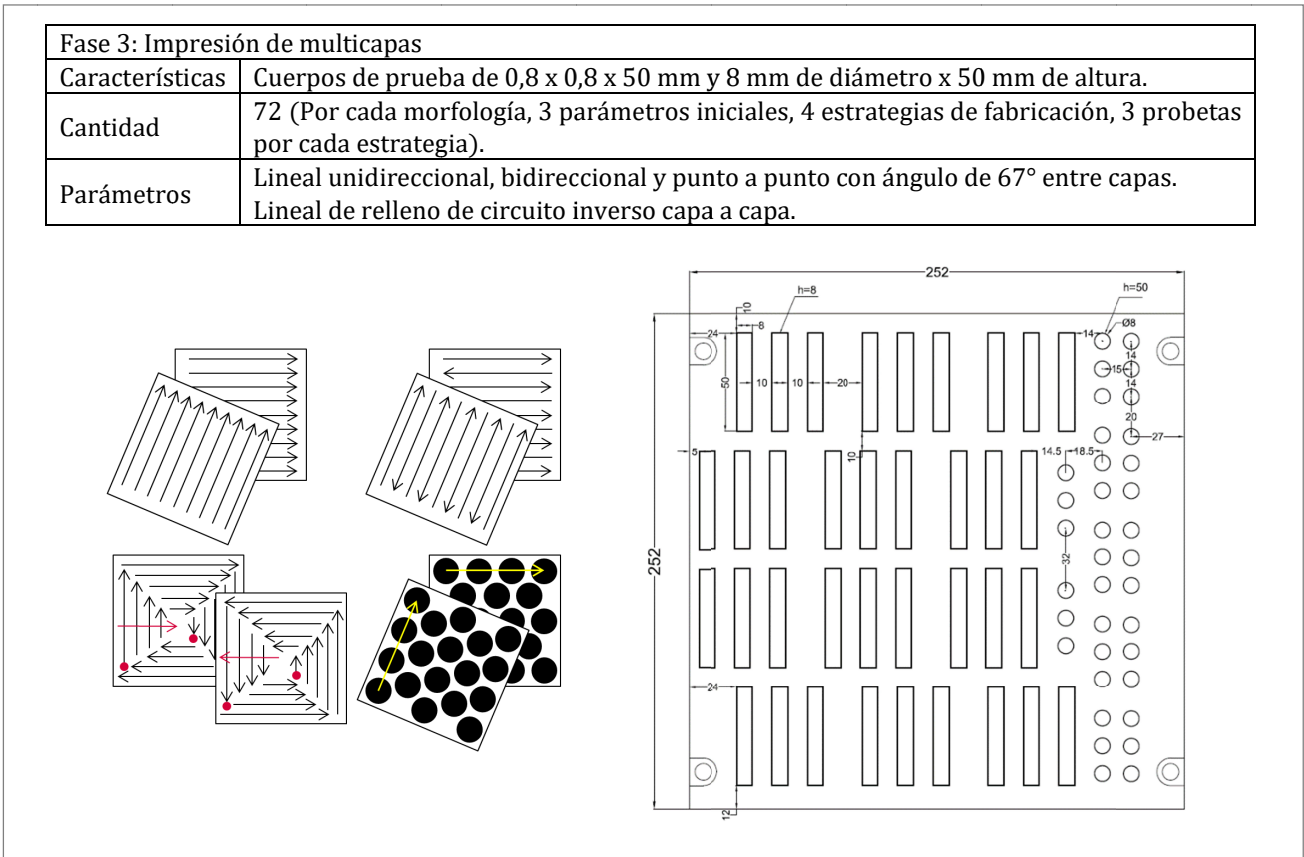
Fase 3, DoE de parámetros a través de deposición multicapa de soldadura.
